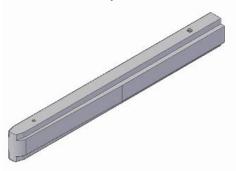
Деформирующая оправка для изготовления заготовок малолистовых рессор
